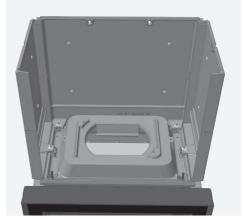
Vissage des parois latérales et arrière sur le FINA
